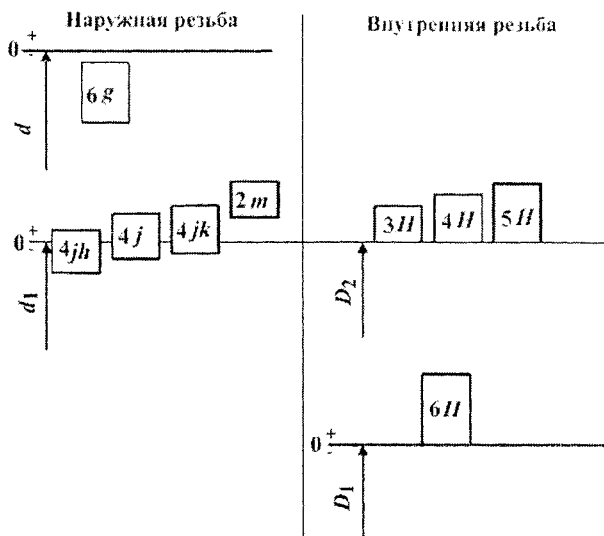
Поля допусков резьб для соединений с переходными посадками
